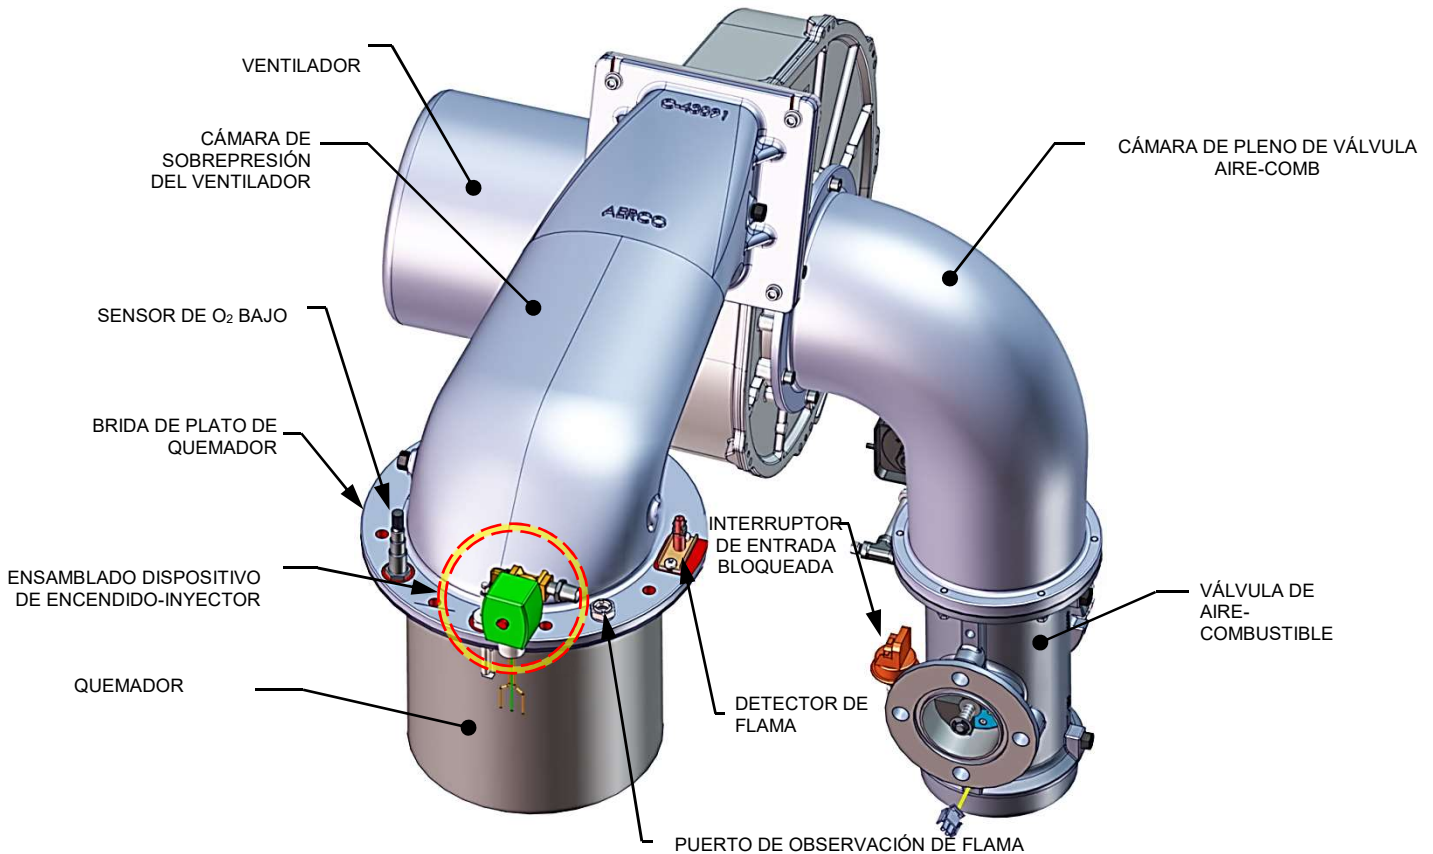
Ensamblado del quemador de BMK 2500/3000 (retirado de la caldera)
